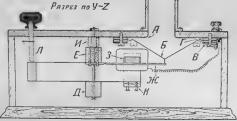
Вид сверху и разрез готового громкоговорителя.
